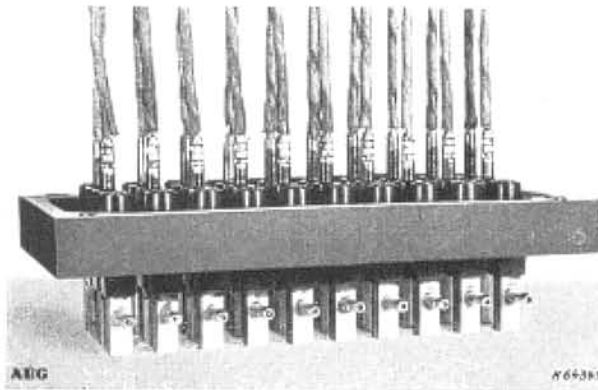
Zangenweichlösungen an eisernen Durchführungen.
